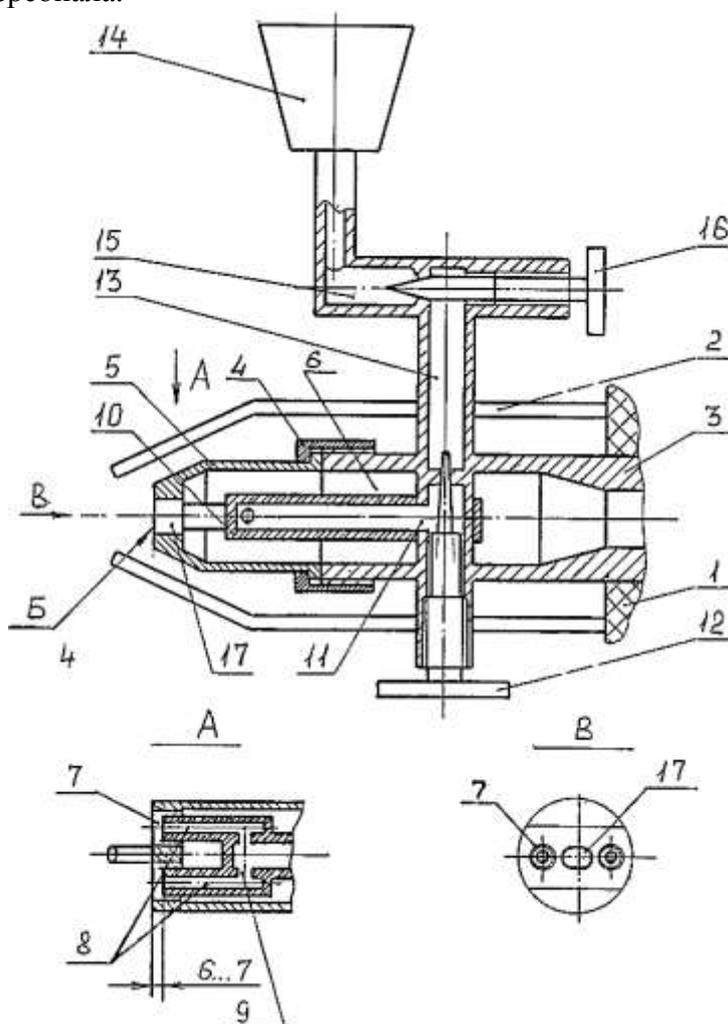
Электродуговой металлizador ЭДМ-6ГД: 1 – изоляционная платформа; 2 – направляющие для электродных проволок; 3 – корпус; 4 – гайка; 5 – крышка; 6 – корпус воздуховода; 7 – кольцевой канал-камера; 8 – топливное сопло; 9, 11 – отверстия; 10 – втулка; 12 – игольчатый вентиль; 13, 15 – каналы подачи топлива; 14 – топливный бачок; 16 – вентиль запорный; 17 – сопло центральное
